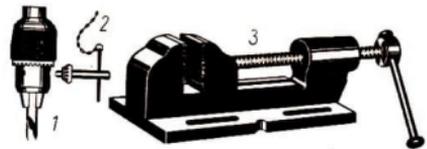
Bohrfutter, Spannschlüssel und Maschinenschraubstock
